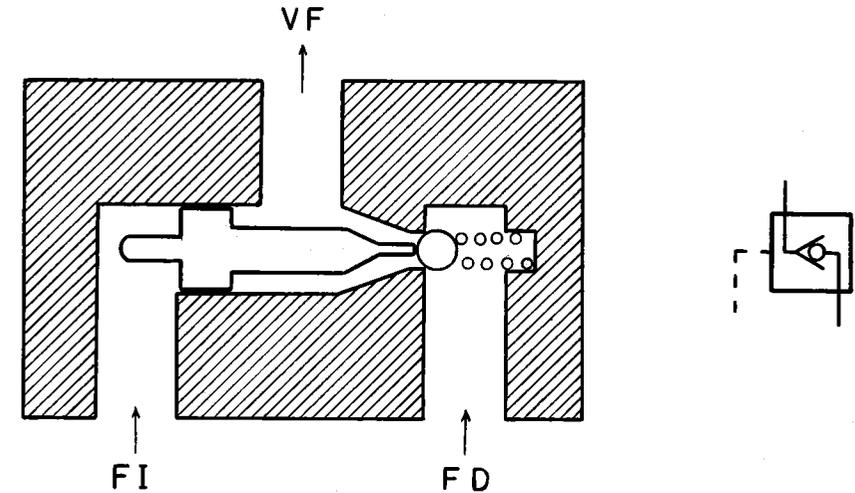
Sección y símbolo de una válvula de un sentido pilotada, que se emplea para que el frenado del remolque sólo se produzca cuando se frenan las ruedas derecha e izquierda del tractor simultáneamente.
